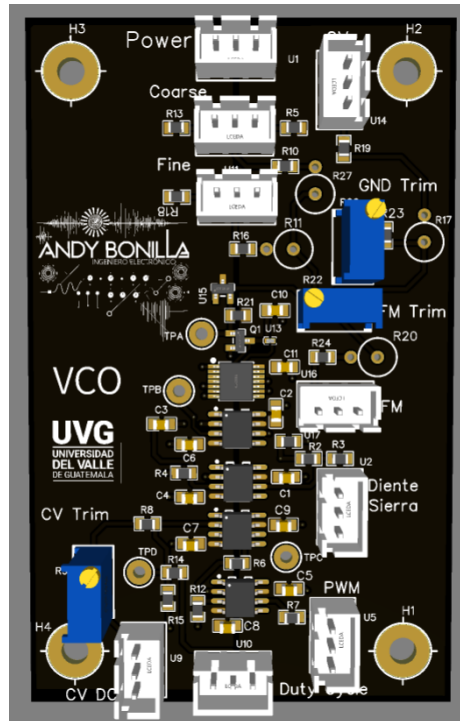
Vista 3D de PCB oscilador controlador por voltaje
